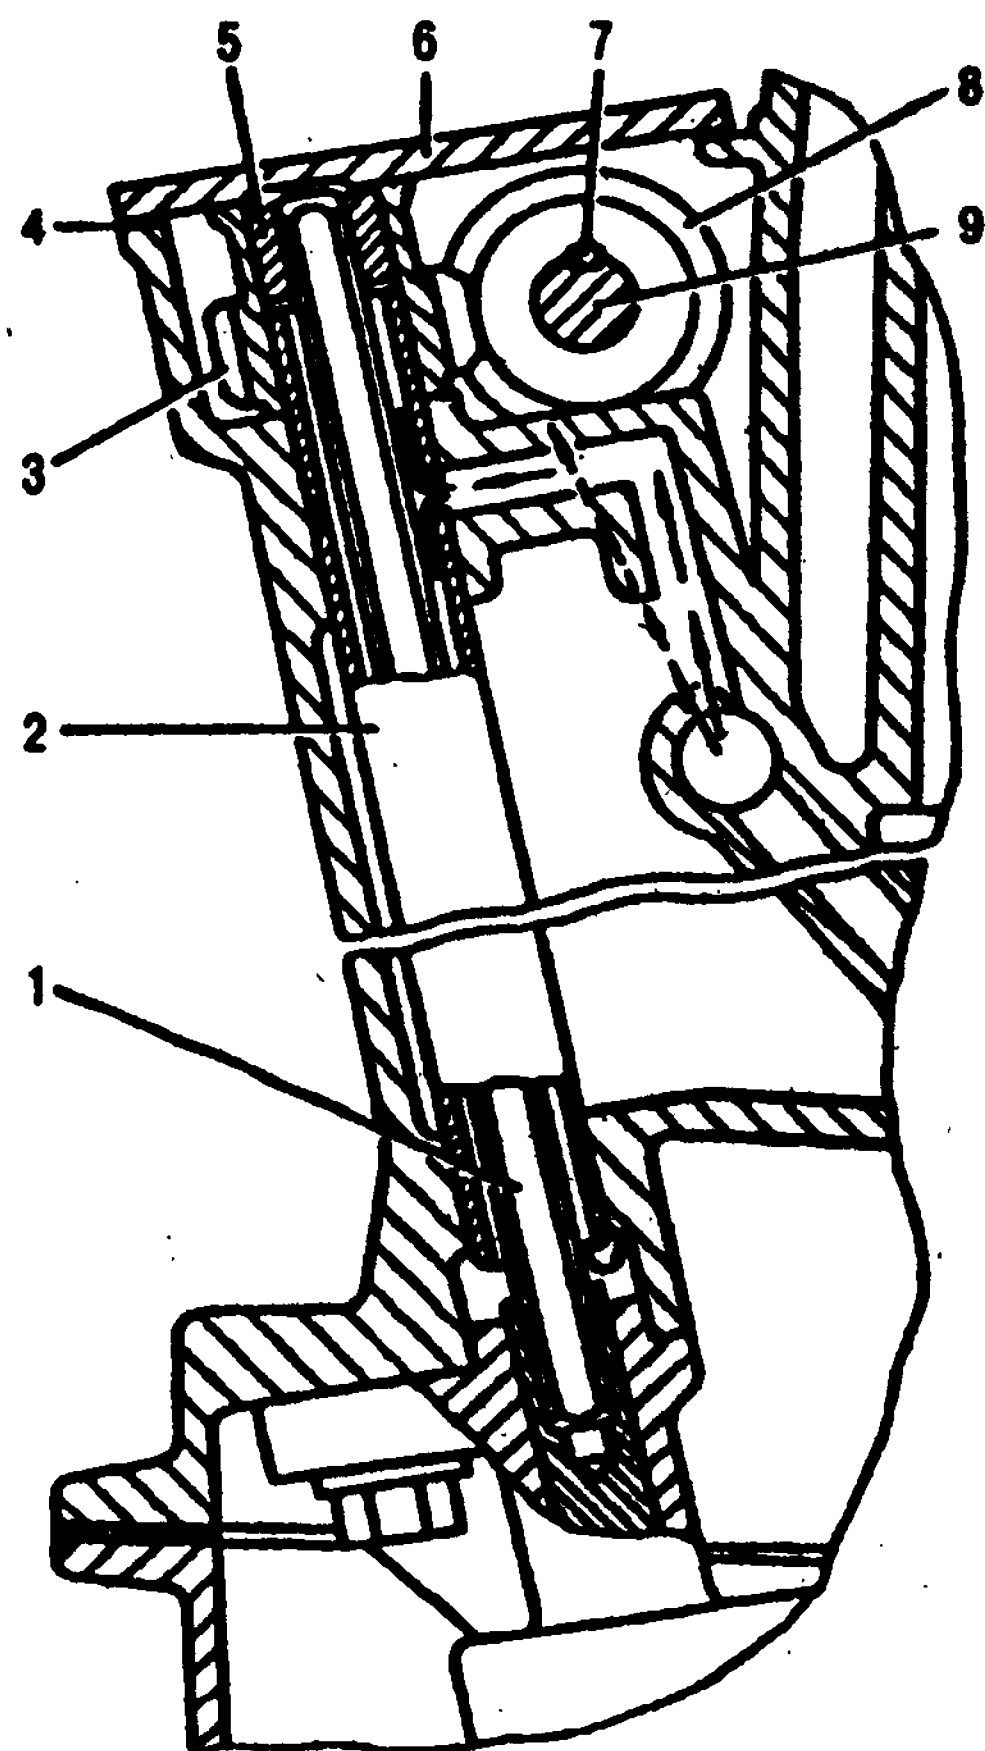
Привод масляного насоса: 1 - валик привода масляного насоса; 2 - валик; 3 - ведомая шестерня; 4 - прокладка; 5 - втулка; 6 - крышка; 7 - шпонка; 8 - ведущая шестерня; 9 - промежуточный вал
